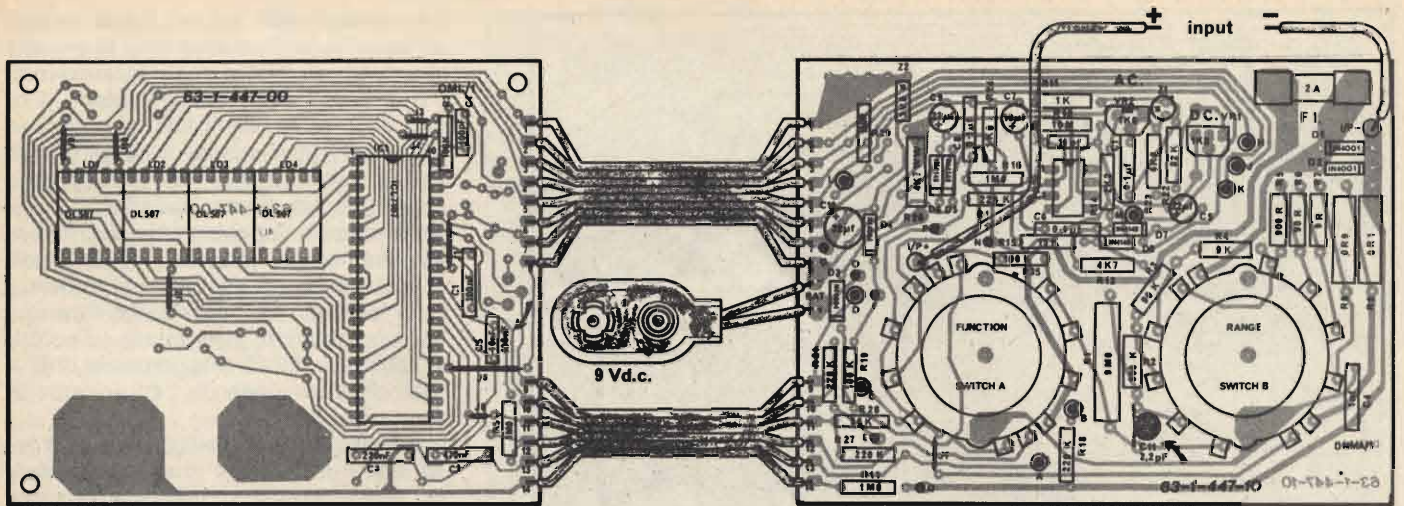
Disposizione dei componenti sulla basetta del KS 205 in unione al KS 225.
